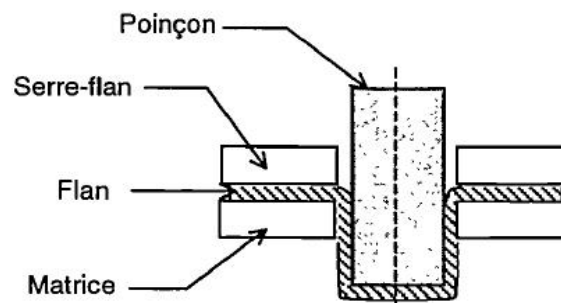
Principe d'emboutissage (pièces forgées) .
